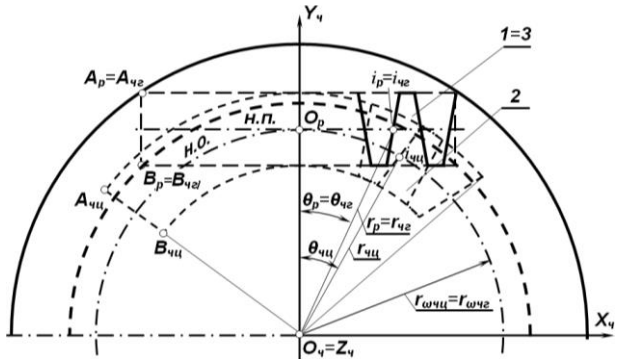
Связь зубьев 1 исходного реечного зубчатого контура с витками 2 цилиндрического и витками 3 гиперболоидного основных червяков
